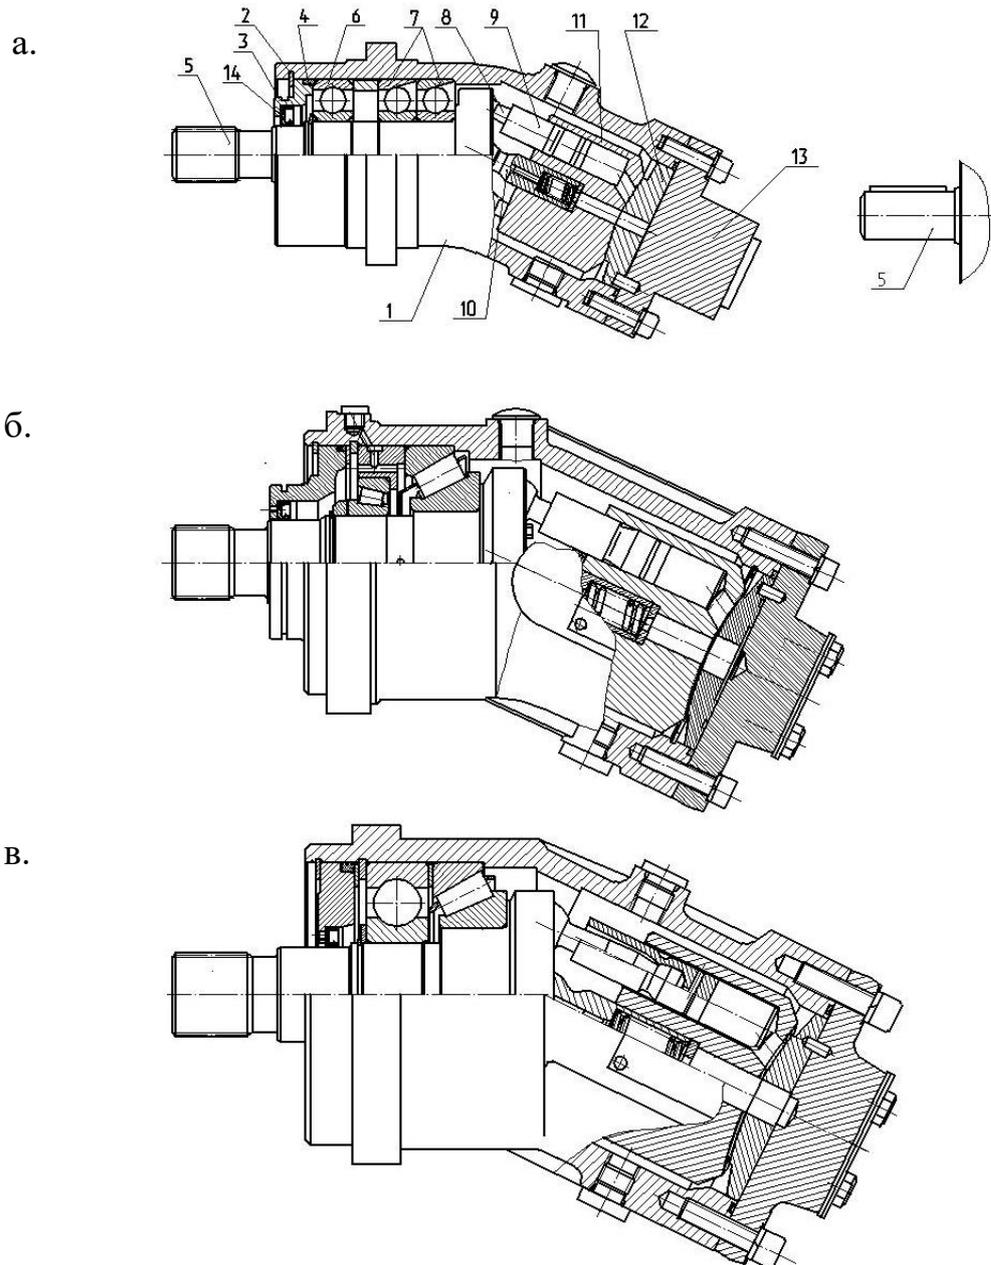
Гидромотор аксиально-поршневой нерегулируемый: 1 – корпус гидромотора; 2 – стопорное кольцо; 3 – крышка; 4 – резиновое кольцо; 5 – вал; 6 – подшипник; 7 – подшипник; 8 – шатун; 9 – поршень; 10 – шип; 11 – блок цилиндров; 12 – распределитель; 13 – крышка; 14 – манжета
